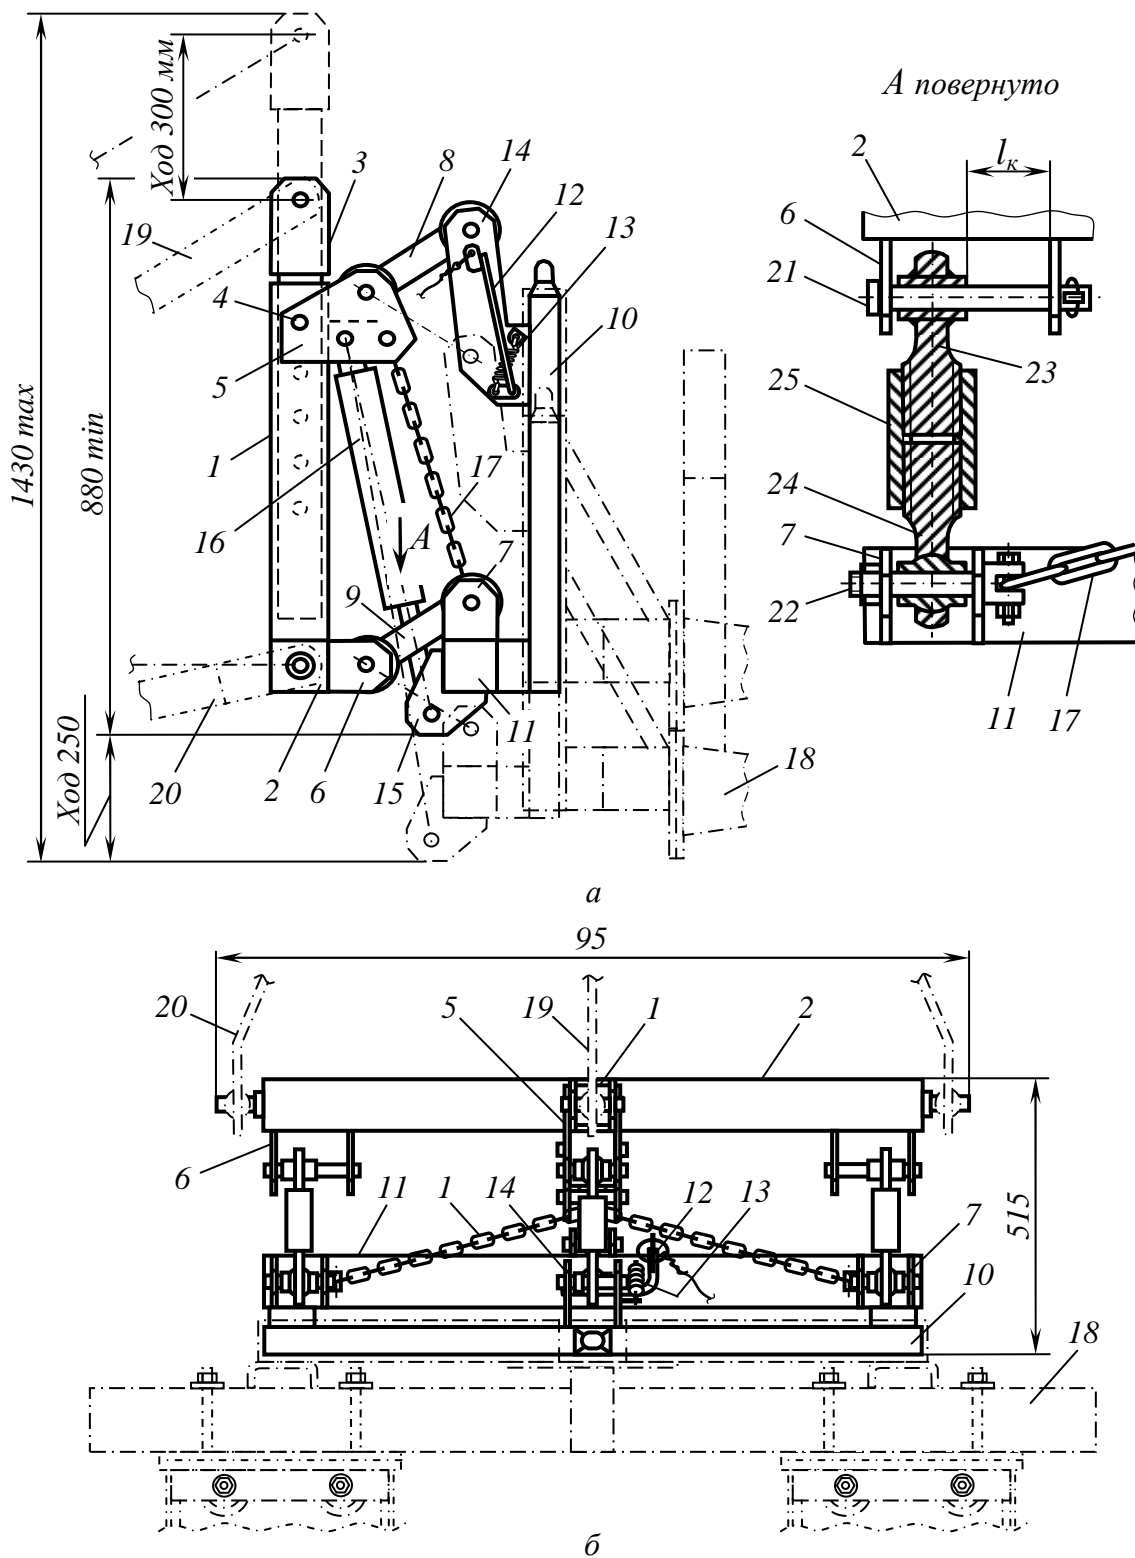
Схема приспособления с гидроприводом к навесному устройству трактора при агрегатировании его с дисковыми орудиями, оснащенными автосцепкой: а, б – виды сбоку и сверху; 1 и 2 – вертикальный и горизонтальный брусья рамы; 3 – выдвижная стойка с проушиной; 4 – фиксатор; 5 – кронштейн; 6 и 7 – проушины; 8 и 9 – верхний и нижние рычаги; 10-15 – соответственно: присоединительный треугольник, брус, рукоятка фиксатора, пружина, верхний и нижний кронштейны рамки автосцепки; 16 – гидроцилиндр; 17 – цепь; 18 – культиватор; 19 и 20 – верхняя и нижние тяги навесного устройства трактора; 21 и 22 – пальцы; 23 и 24 – головки с цилиндрической и шаровой
